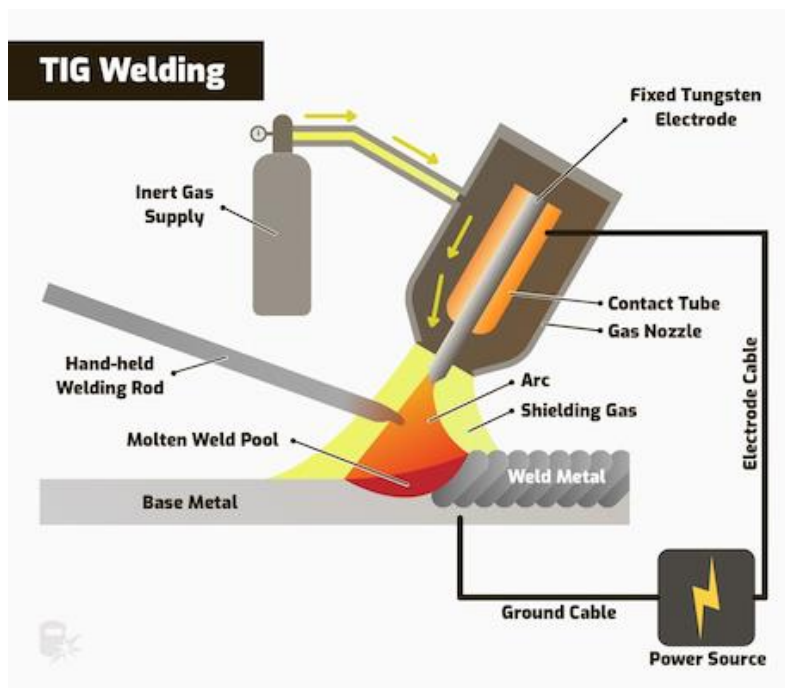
Схема выполнения аргонодуговой сварки неплавящимся электродом
